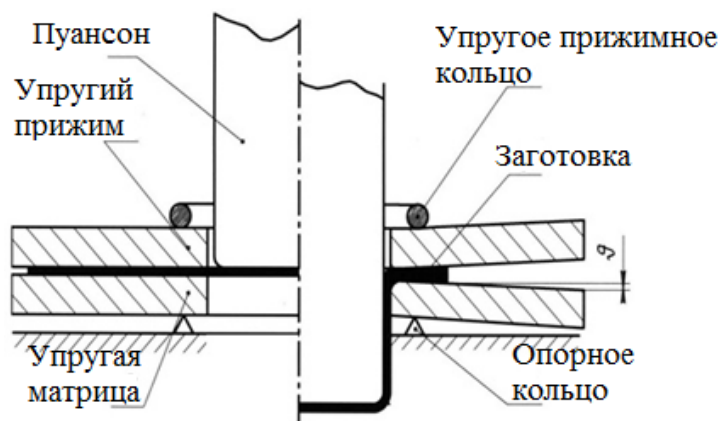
Штамп для глубокой вытяжки осесимметричных деталей
